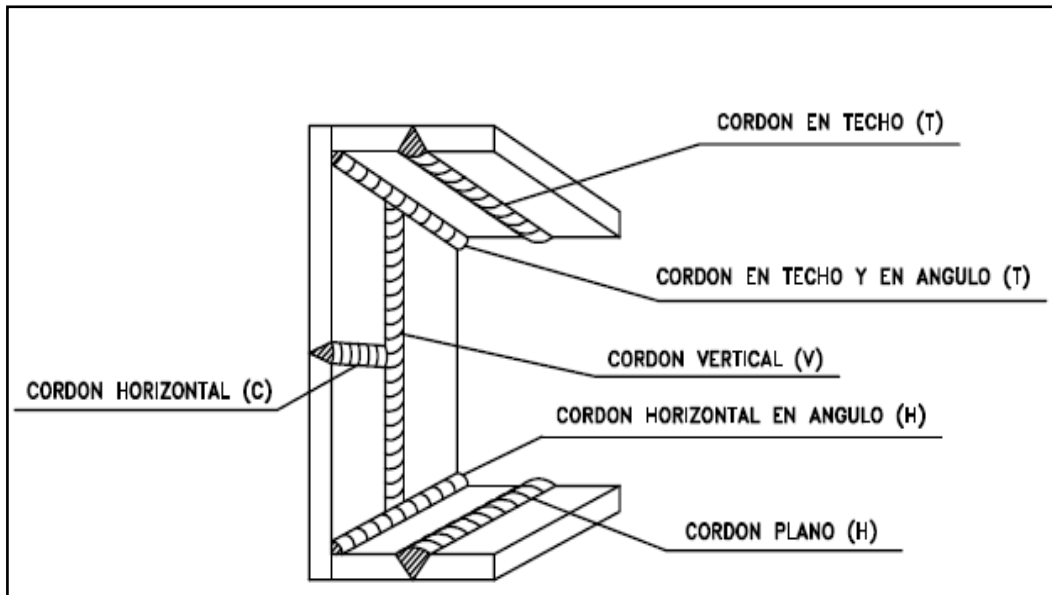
Cordón de soldadura según su posición de soldar
